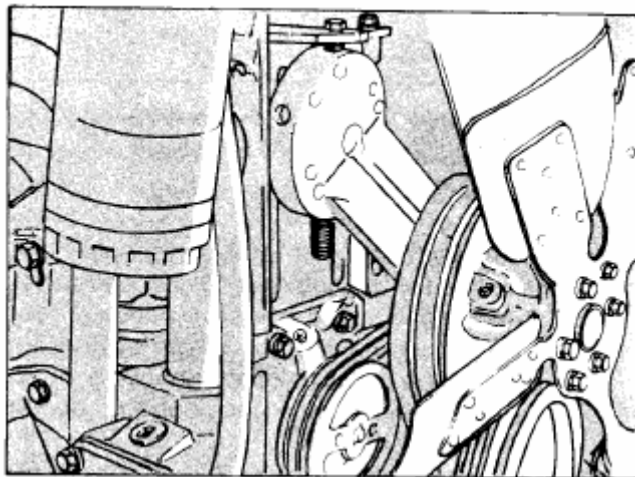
(ОМ10161). Установка втулки вентилятора двигателя NTC-350FFC
